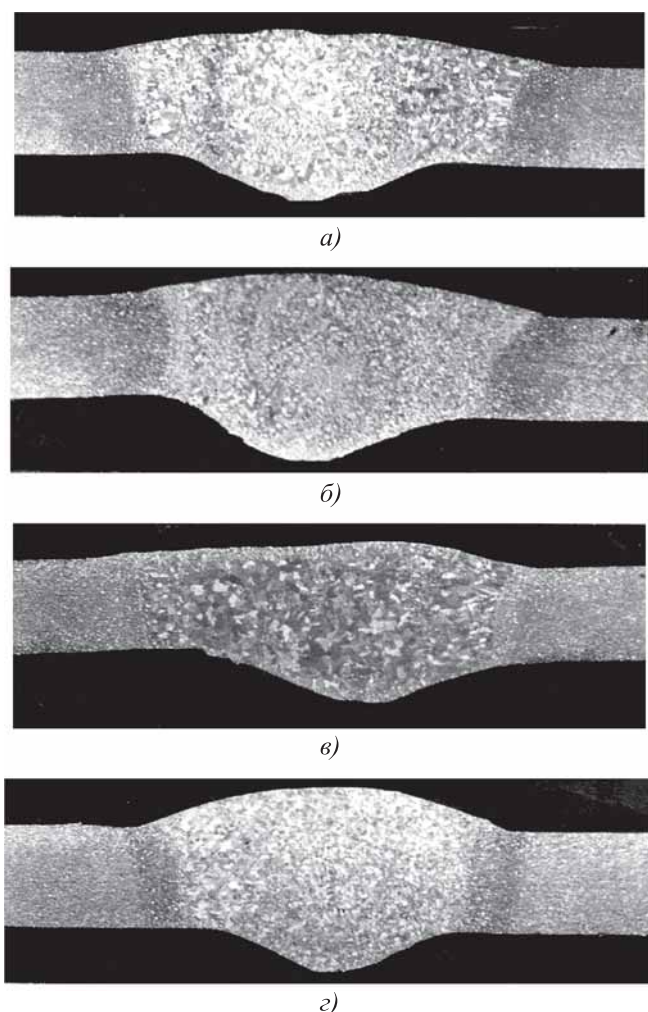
Макроструктуры стыковых соединений листов сплава 1420 толщиной 4 мм при механизированной однопроходной сварке с различными присадочными проволоками (×6):
